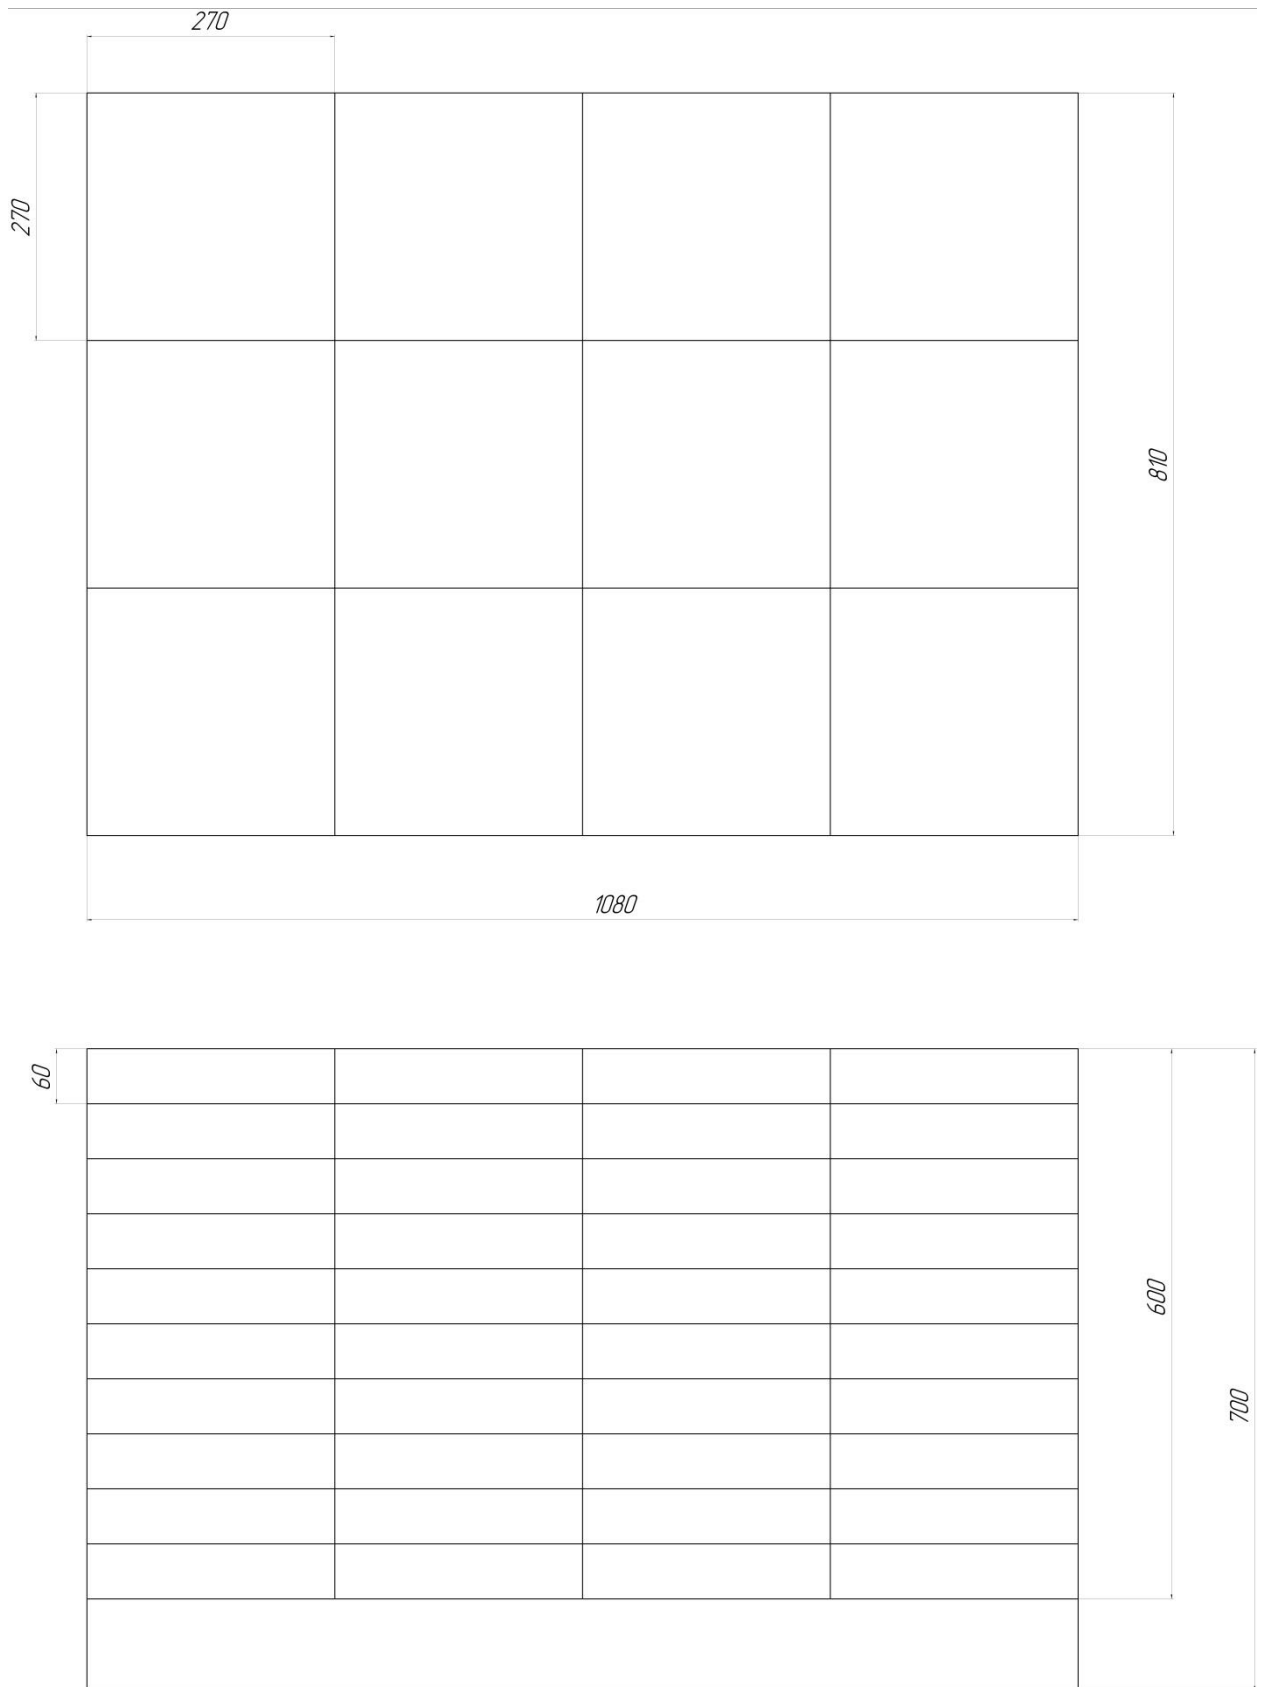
Схема расположения упаковок сцеплений на поддоне
